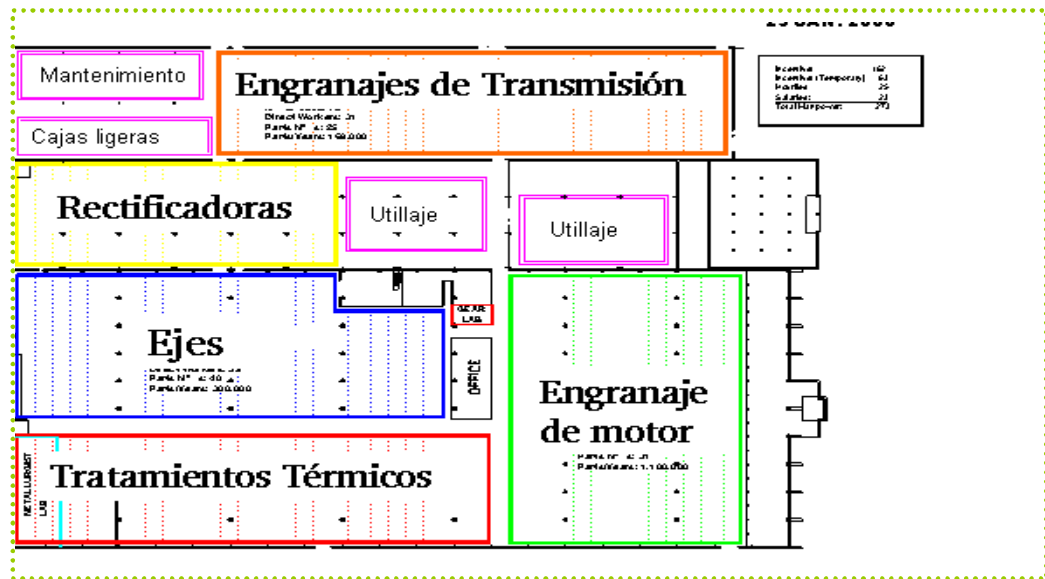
Lay-Out de la minifábrica de Ejes y Engranajes
